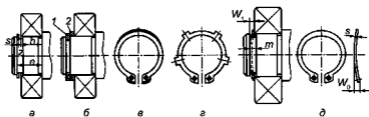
Крепление подшипников на валах пружинными упорными плоскими кольцами: *а* – установочные размеры кольца; *б* – постановка дополнительного компенсаторного кольца 2; *в, г, д* – форма колец
